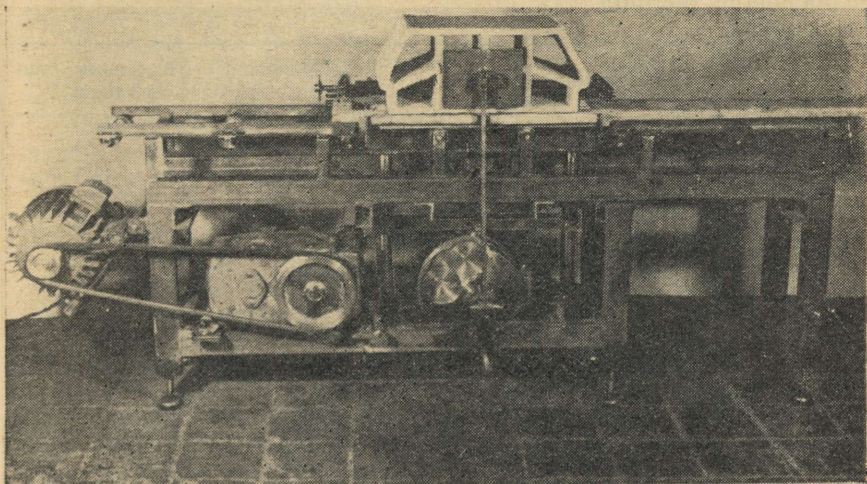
Автомат для укладки блоков перекрытия на сушильные рамы.
